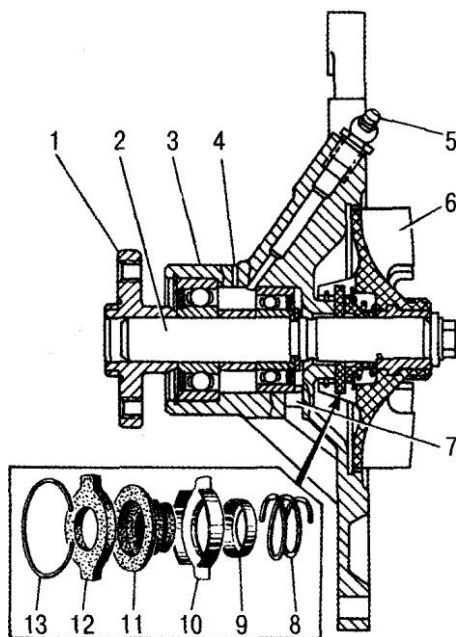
Водяной насос: 1 - ступица вентилятора; 2 - валик; 3 - корпус; 4 - контрольное отверстие выхода смазки из корпуса; 5 - пресс-масленка; 6 - крыльчатка; 7 - контрольное отверстие для выхода жидкости при течи сальника; 8 - пружина; 9, 10 - обоймы сальника; 11 - манжета; 12 - шайба сальника; 13 - запорное кольцо сальника
